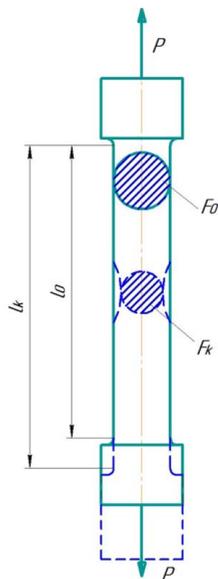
Цилиндрический образец для испытания материала при растяжении
